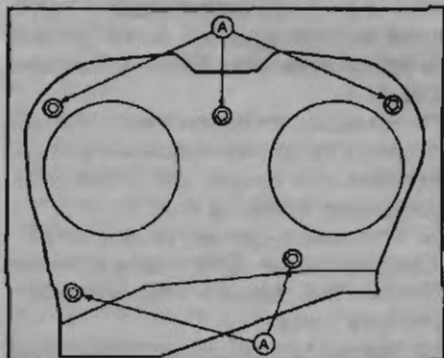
Расположение болтов крепления верхнего зубчатого ремня
